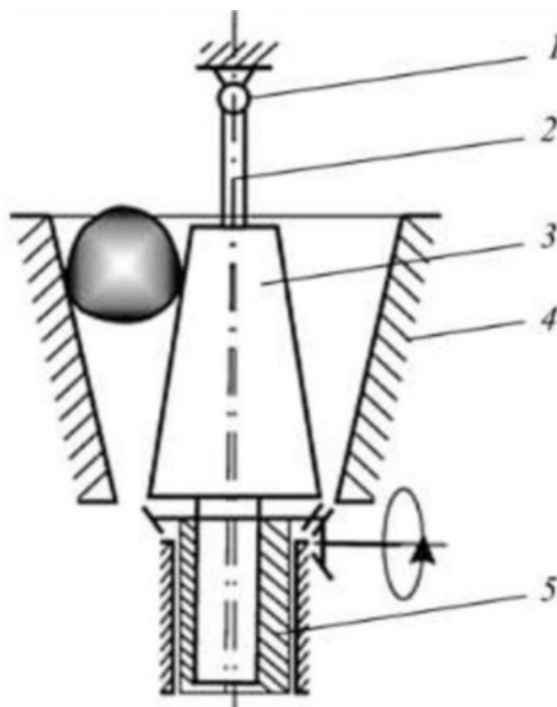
Схема конусной дробилки мелкого дробления: 1 – узел подвеса подвижного конуса; 2 – вал; 3 – подвижный конус; 4 – неподвижный конус; 5 – эксцентриковый стакан
